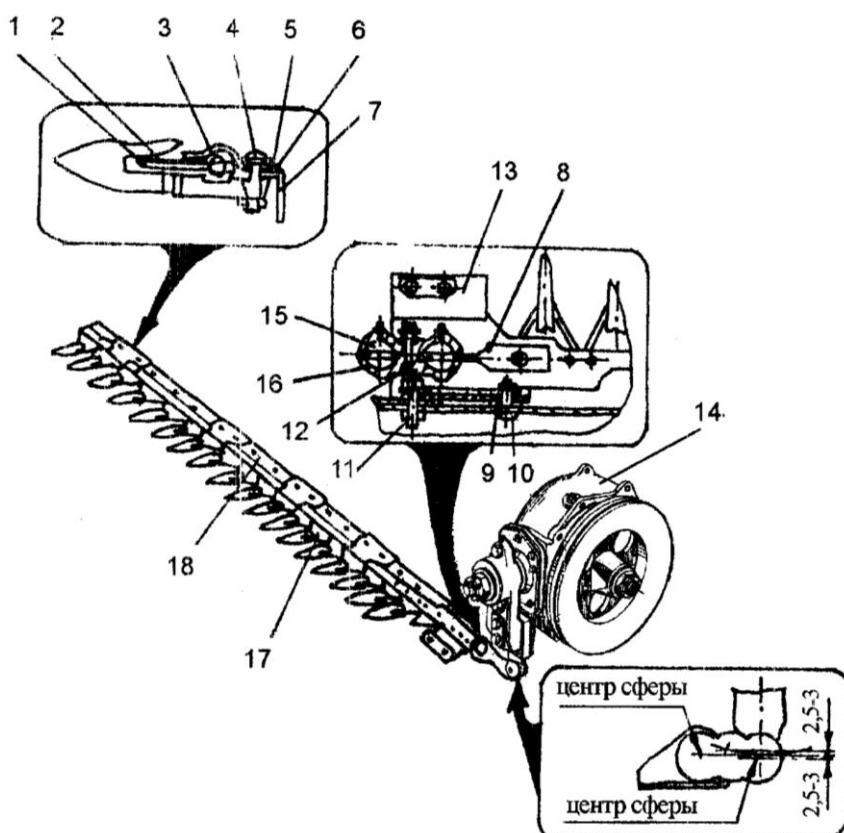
Режущий аппарат: 1 – пластина противорежущая; 2 – сегмент; 3 – прижим; 4, 10, 11, 12 – болты; 5 – пластина трения; 6 – прокладка; 7 – угольник; 8 – головка ножа; 9 – шайба; 13 – направляющая; 14 – механизм качающейся шайбы; 15, 16 – щеки; 17 – нож; 18 – пальцевый брус
